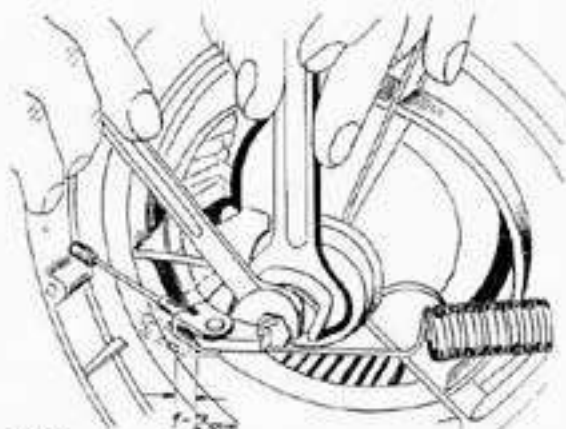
Kupplung mit Ausrückhebel einstellen (Sperr-Klauen-Getriebe), Spiel 1-2 mm.
